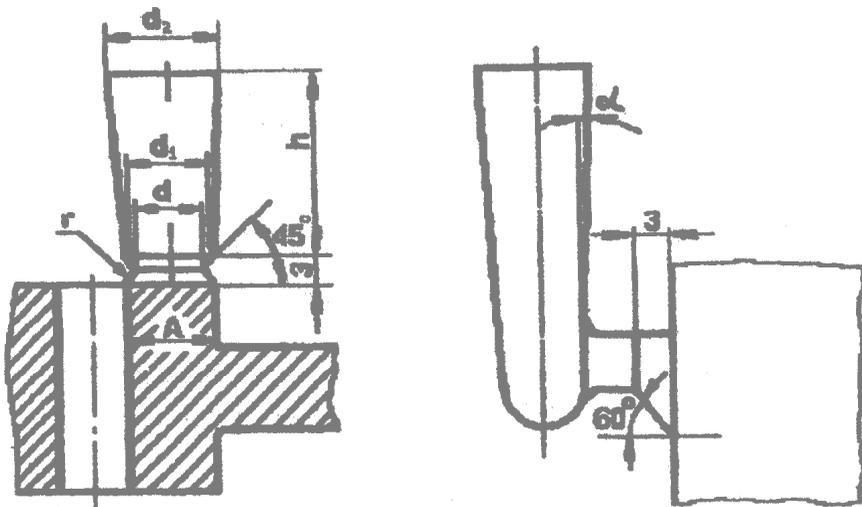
Питающие бобышки для отливок из ковкого чугуна:
